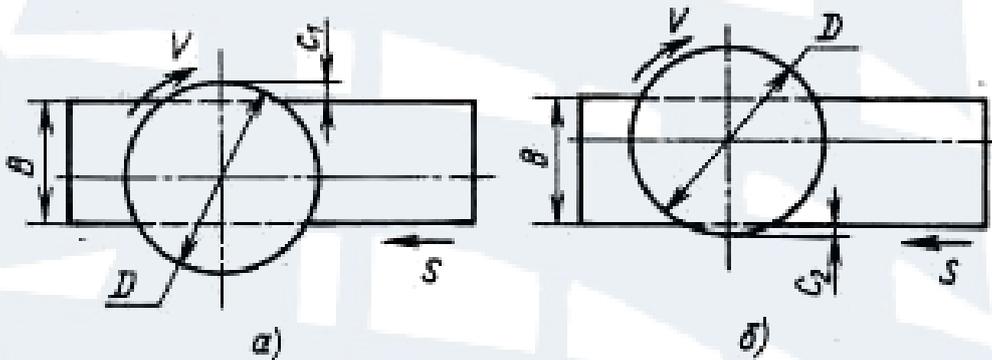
Расположение стальной заготовки при торцовом фрезеровании относительно фрезы:
